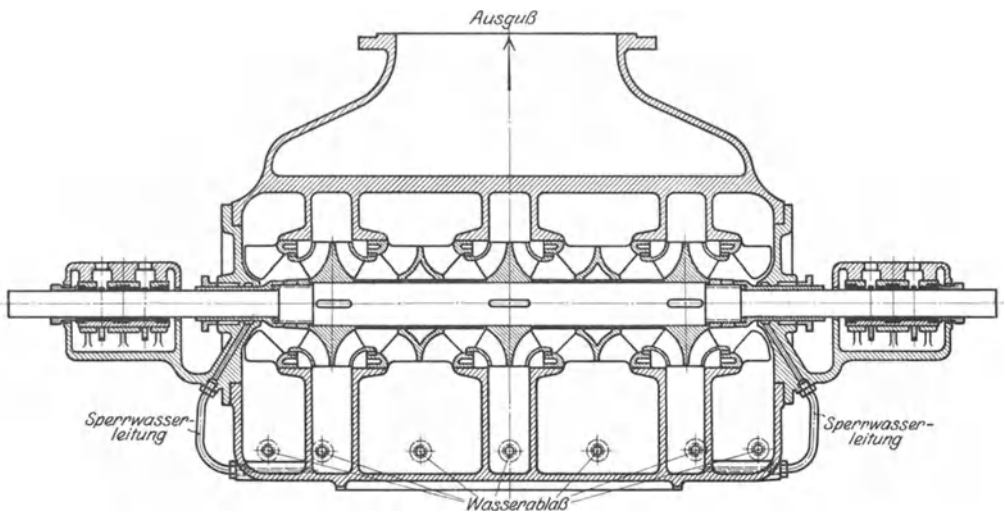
Raschlaufende Kühlwasserpumpe von C. H. Jaeger & Co., für große Wassermengen.
